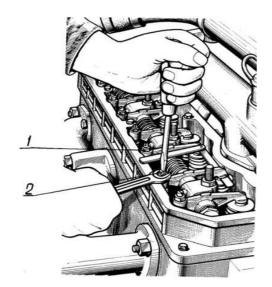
Регулировка зазора в клапанах 1-контргайка; 2-винт
